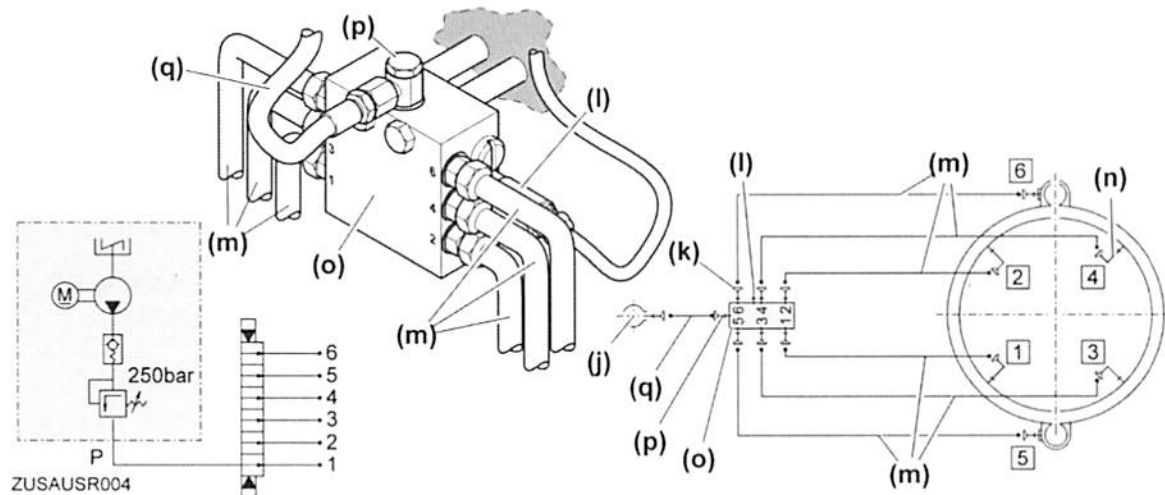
Verlegeplan und Hydraulik-Schaltplan (6er-Verteiler mit zwei Drehwerken)
